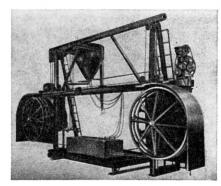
Канатная пила для выпиливания блоков камня в карьере: 1— приводная станция; 2— неразвивающийся канат; 3— натяжное приспособление; 4— пильные стойки
